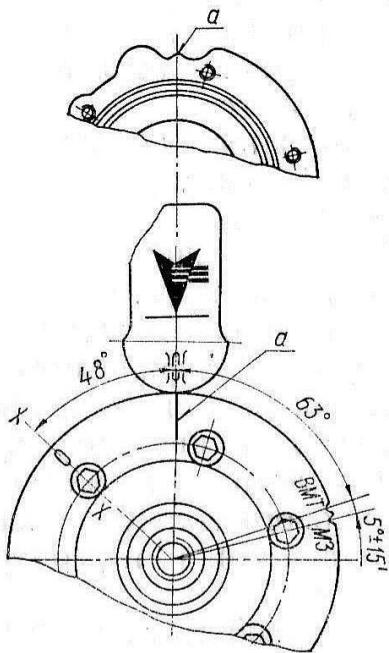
Установочные метки на корпусе и крышке центробежного маслоочистителя:
